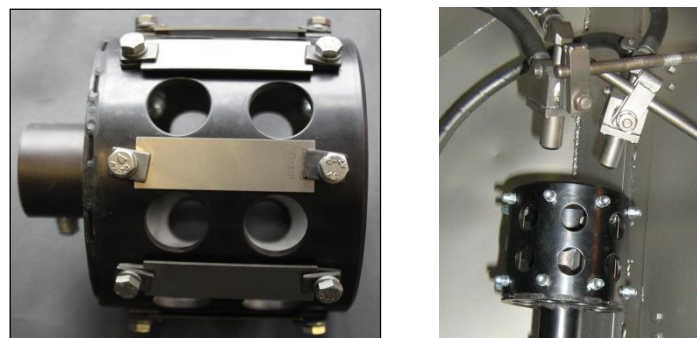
Оснастка в сборе с образцами и камера экспериментального устройства
